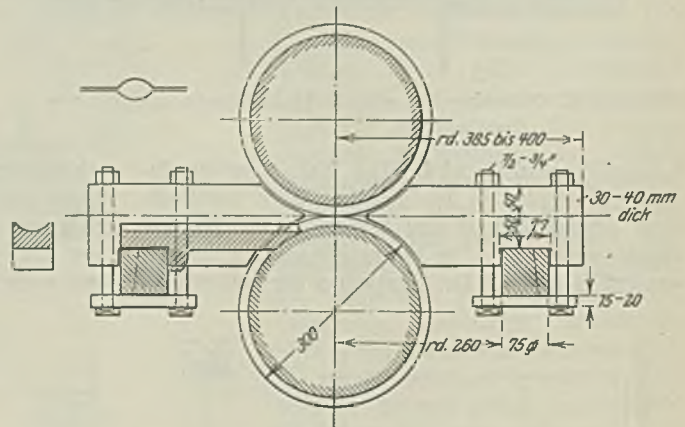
Ein- und Ausführung mit einfachen Quadratwalzbalken.
